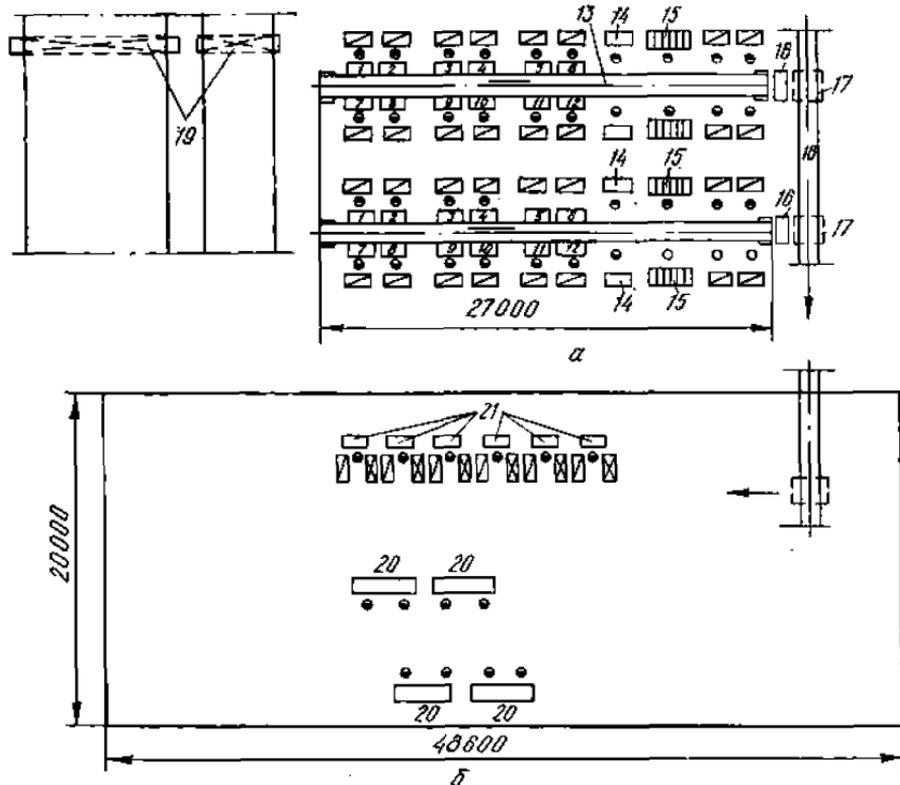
Схема участка предварительной сборки, комплектовки и упаковки в разобранном виде 24 000 наборов (4 изделия) корпусной мебели в год:
